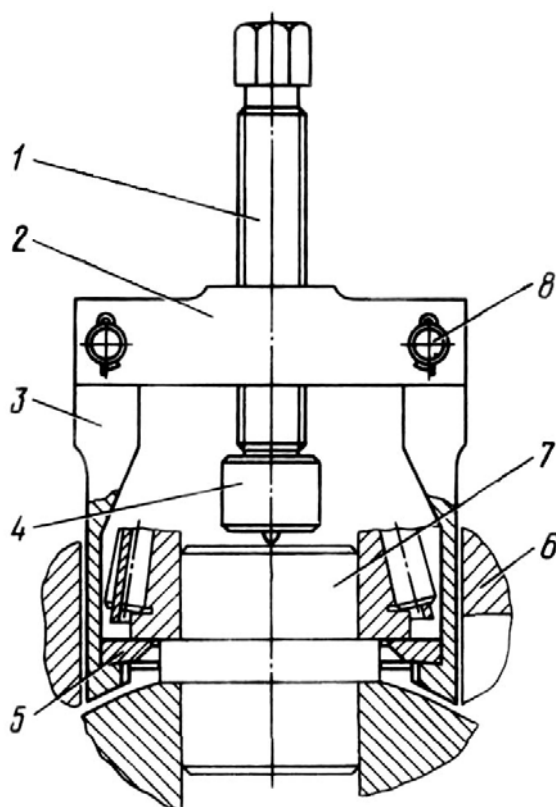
Спрессовка подшипников со шкворней шаровой опоры:
